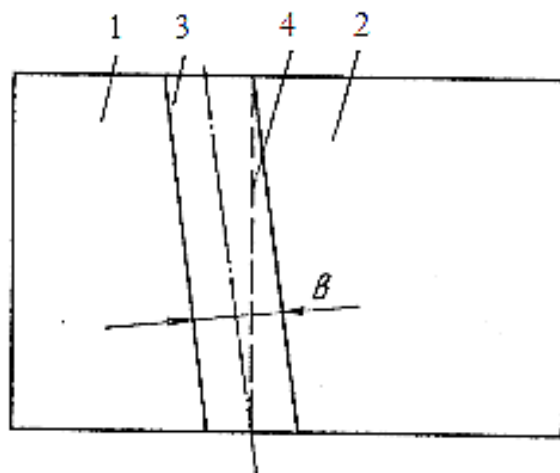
Схематическое изображение контрольного образца [43]: 1, 2 – свариваемые пластины; 3 – сварной шов; 4 – стык пластин; b – ширина шва
